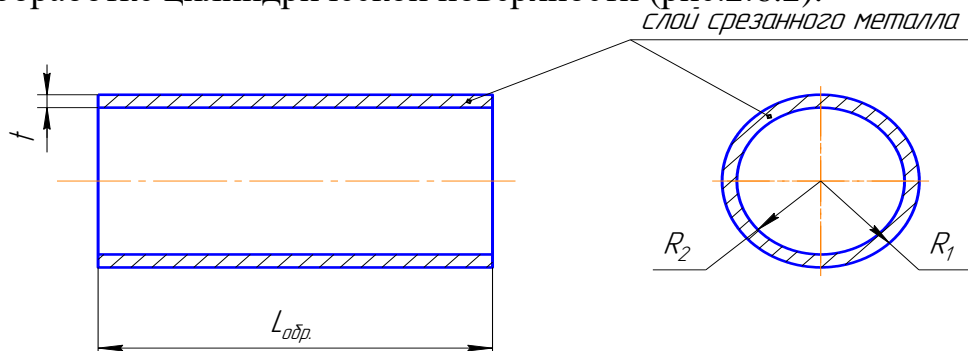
Слой срезанного металла при обработке цилиндрической поверхности
